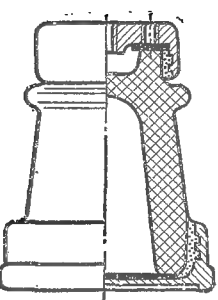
Опорный изолятор с наружной заделкой арматуры.
